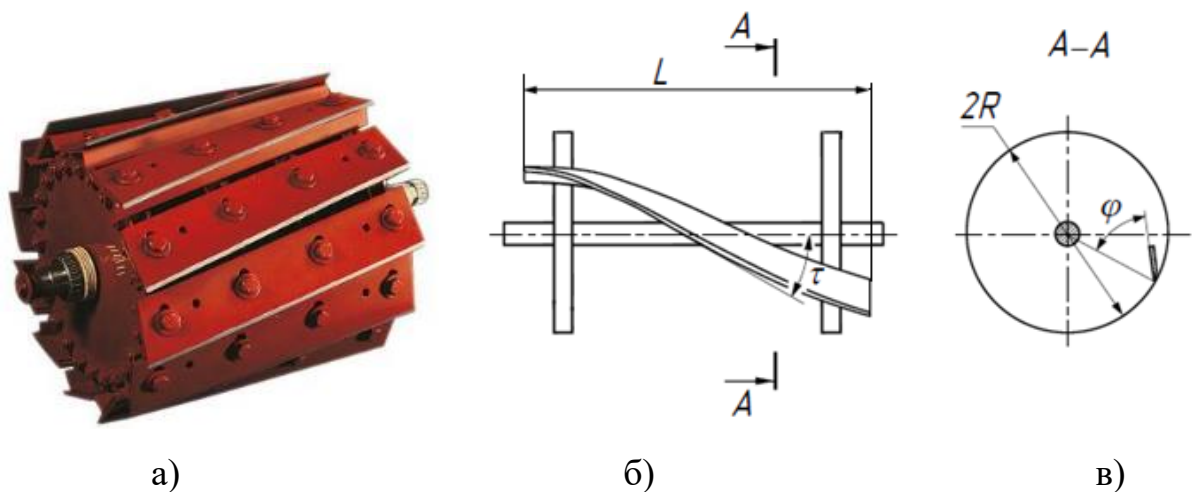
Подрібнювальний барабан та конструктивні параметри окремого ножа: а) подрібнювальний барабан із ножами; б) окремий ніж на барабані; в) поперечний переріз ножа
